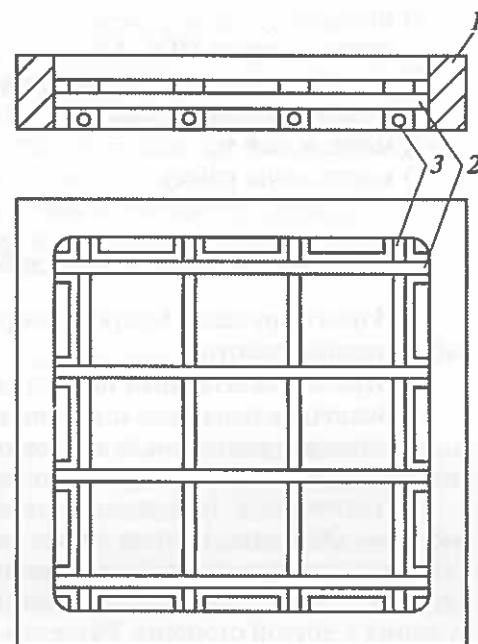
Эскиз раскладки монтажных проводов сетки в монтажной рамке:
